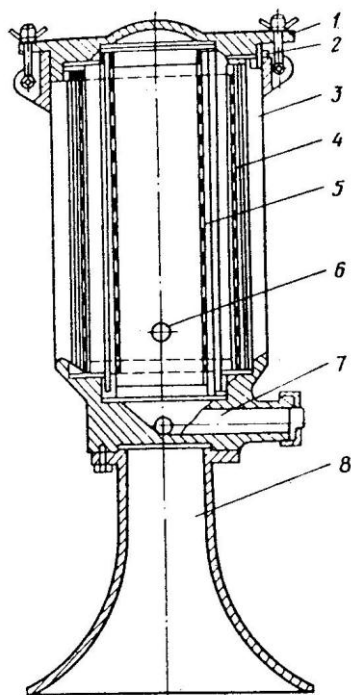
Циліндричний фільтр: 1 - кришка; 2 - гумова прокладка; 3 - корпус; 4 - зовнішня сітка; 5 - внутрішня сітка; 6 - патрубок, що відводить; 7 - патрубок, що підводить; 8 - підставка.
